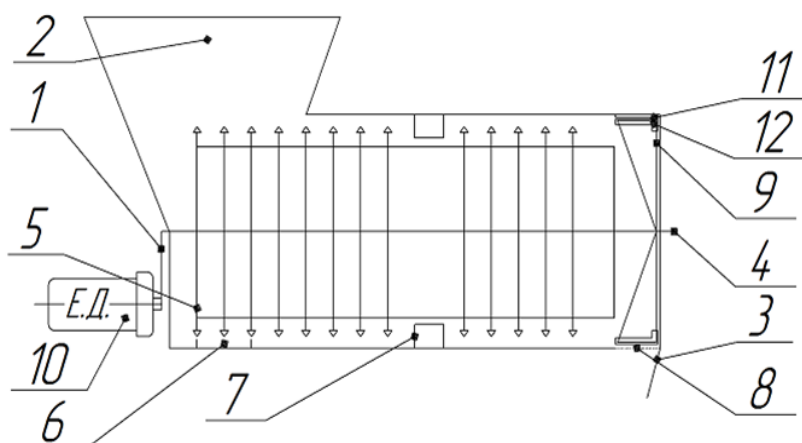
Конструкційна схема подрібнювача грубих стеблових кормів: 1 – циліндрична камера; 2 – завантажувальна горловина; 3 – вивантажувальний патрубок; 4 – горизонтальний вал; 5 – ножі; 6 – протиризи; 7 – пластини формування потоку; 8 – вивантажувальне решето; 9 – лопаті; 10 – електродвигун; 11 – бичі; 12 – подрібнювальні елементи
